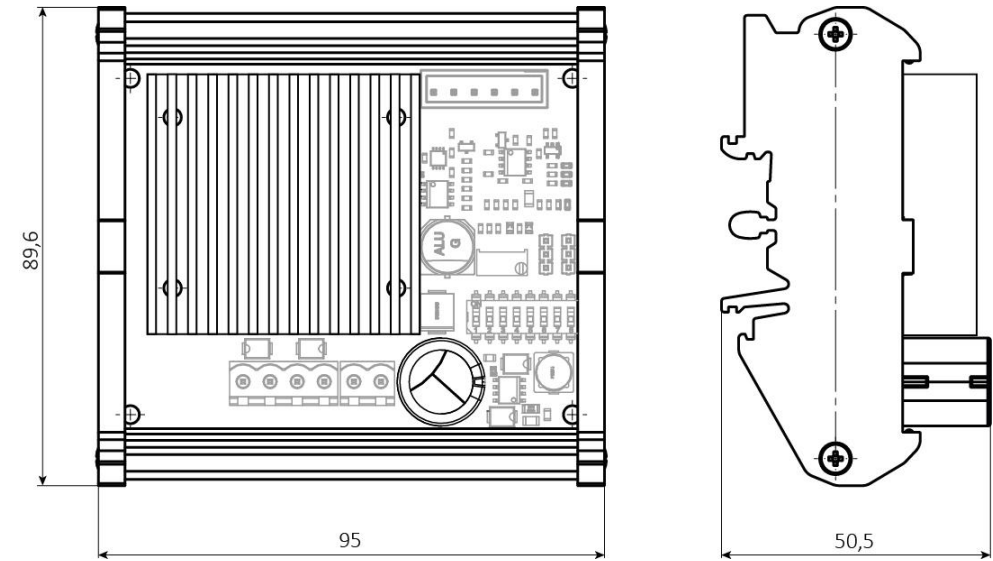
Габаритные и присоединительные размеры драйвера шагового двигателя SMD-2.8 с DIN-фиксатором.
